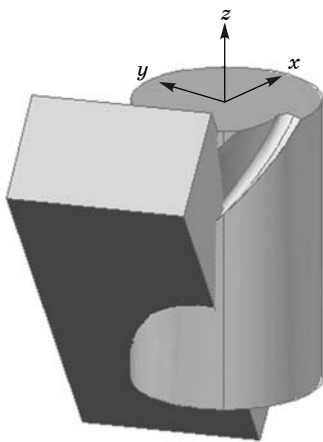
Взаимное расположение детали с ВП и заготовки для инструментальной рейки
